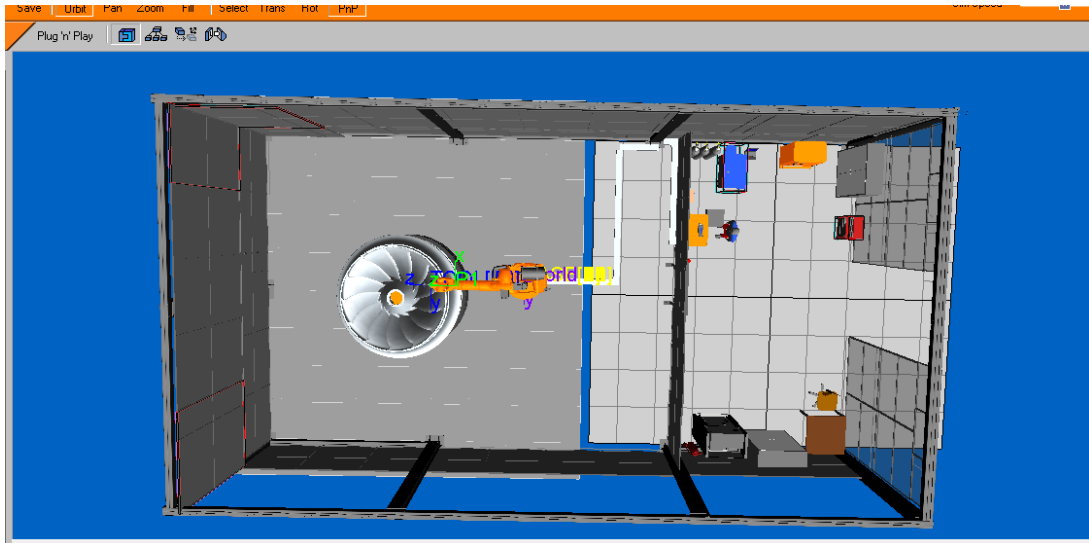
Vista superior de la cabina de metalizado. (Fuente: Autor)
